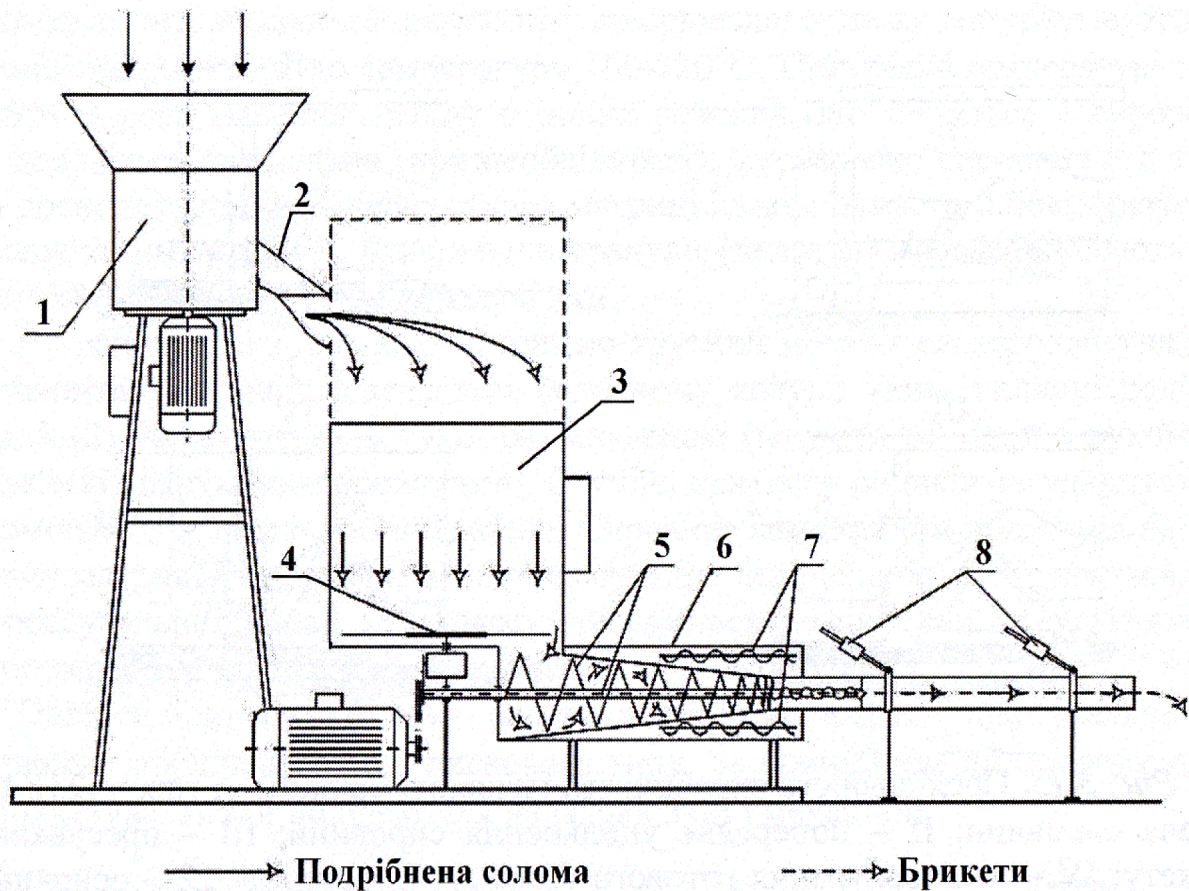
Технологічна схема виробництва паливних брикетів із соломи: 1 – роторна дробарка; 2 – направляючий лоток; 3 – завантажувальний бункер; 4 – ворушильник; 5 – конічний шнек; 6 – корпус прес-брикетувальника; 7 – електронагрівачі; 8 – механізм для регулювання щільності брикетів (підпресовувач)
